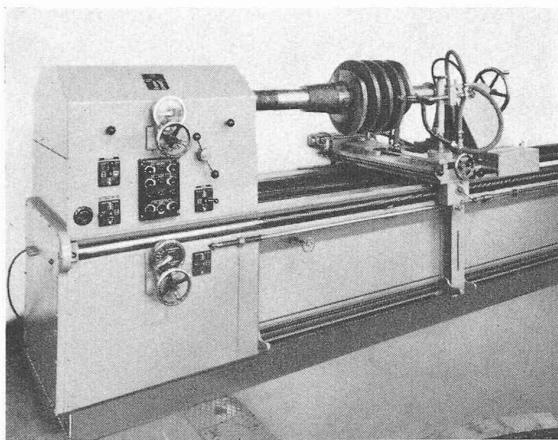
Trempe d'une vis sans fin pour engrenage sur la machine à tremper universelle.
